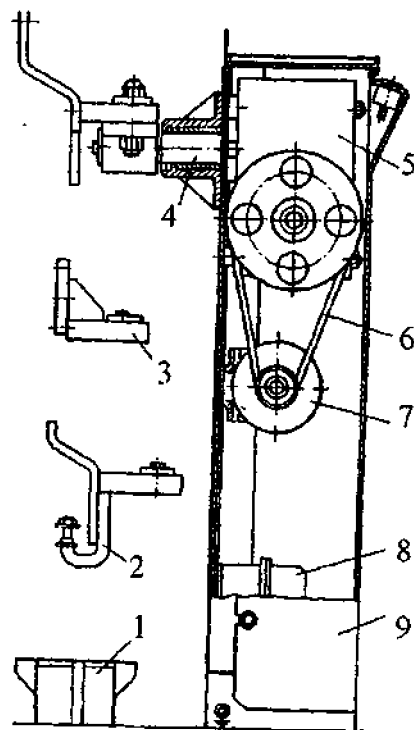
Стенд Р-641 для разборки и сборки двигателей
